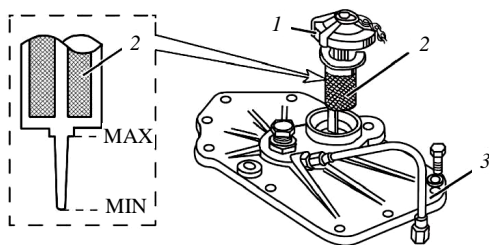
Проверка уровня масла в корпусе ГУР:
